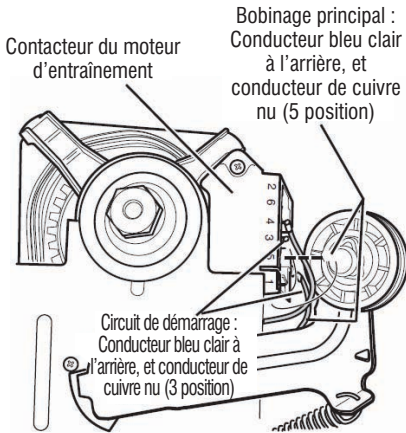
Points de mesure pour le bobinage du moteur (bobinage principal et bobinage de démarrage)
